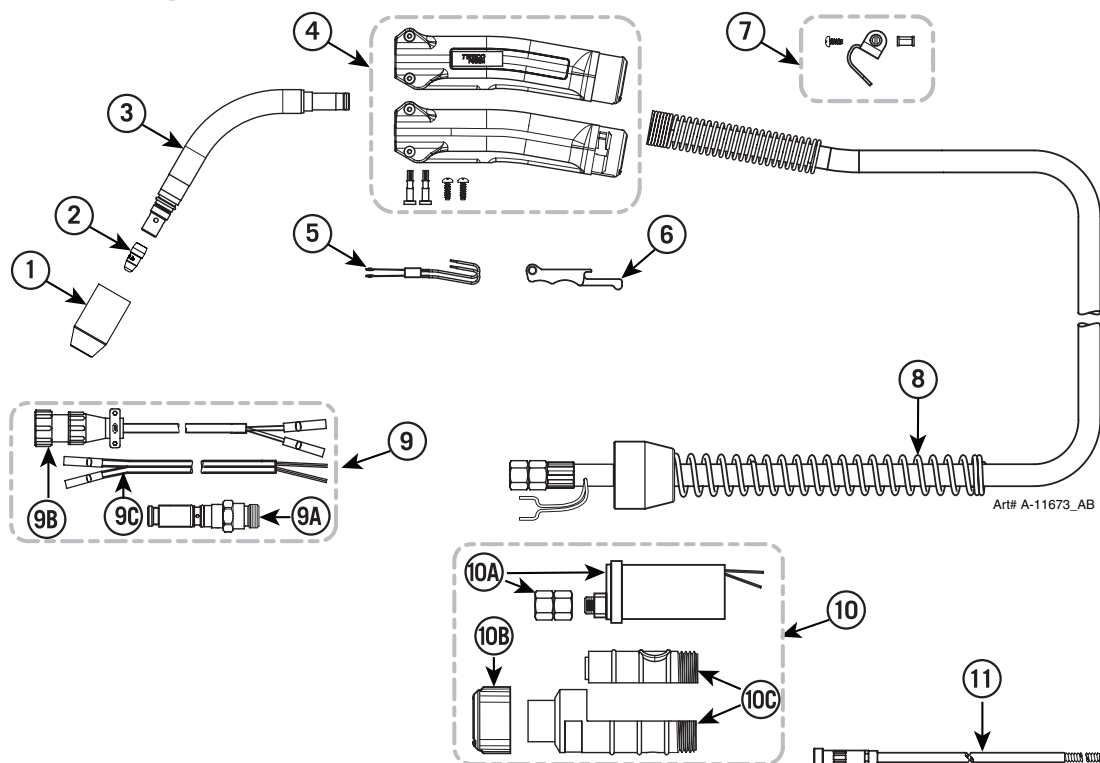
Pistola MIG de Fusion de Tweco 250 A
